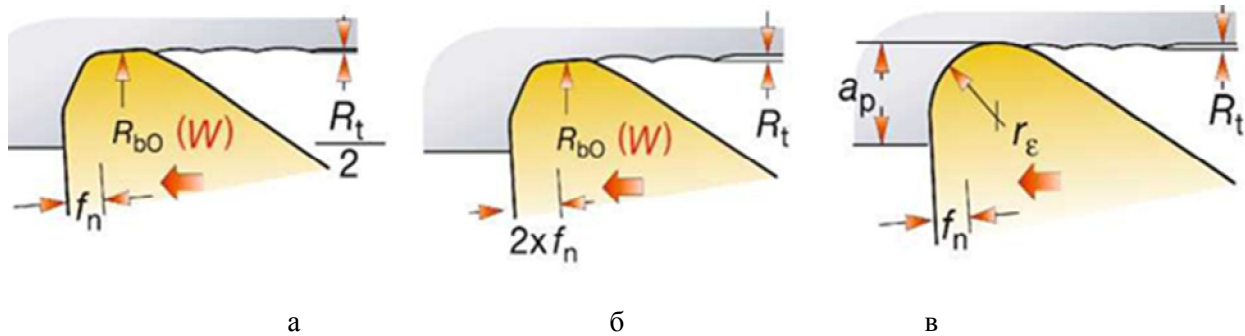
Режущая вершина СМП Wiper (а, б) и стандартной СМП (в)
